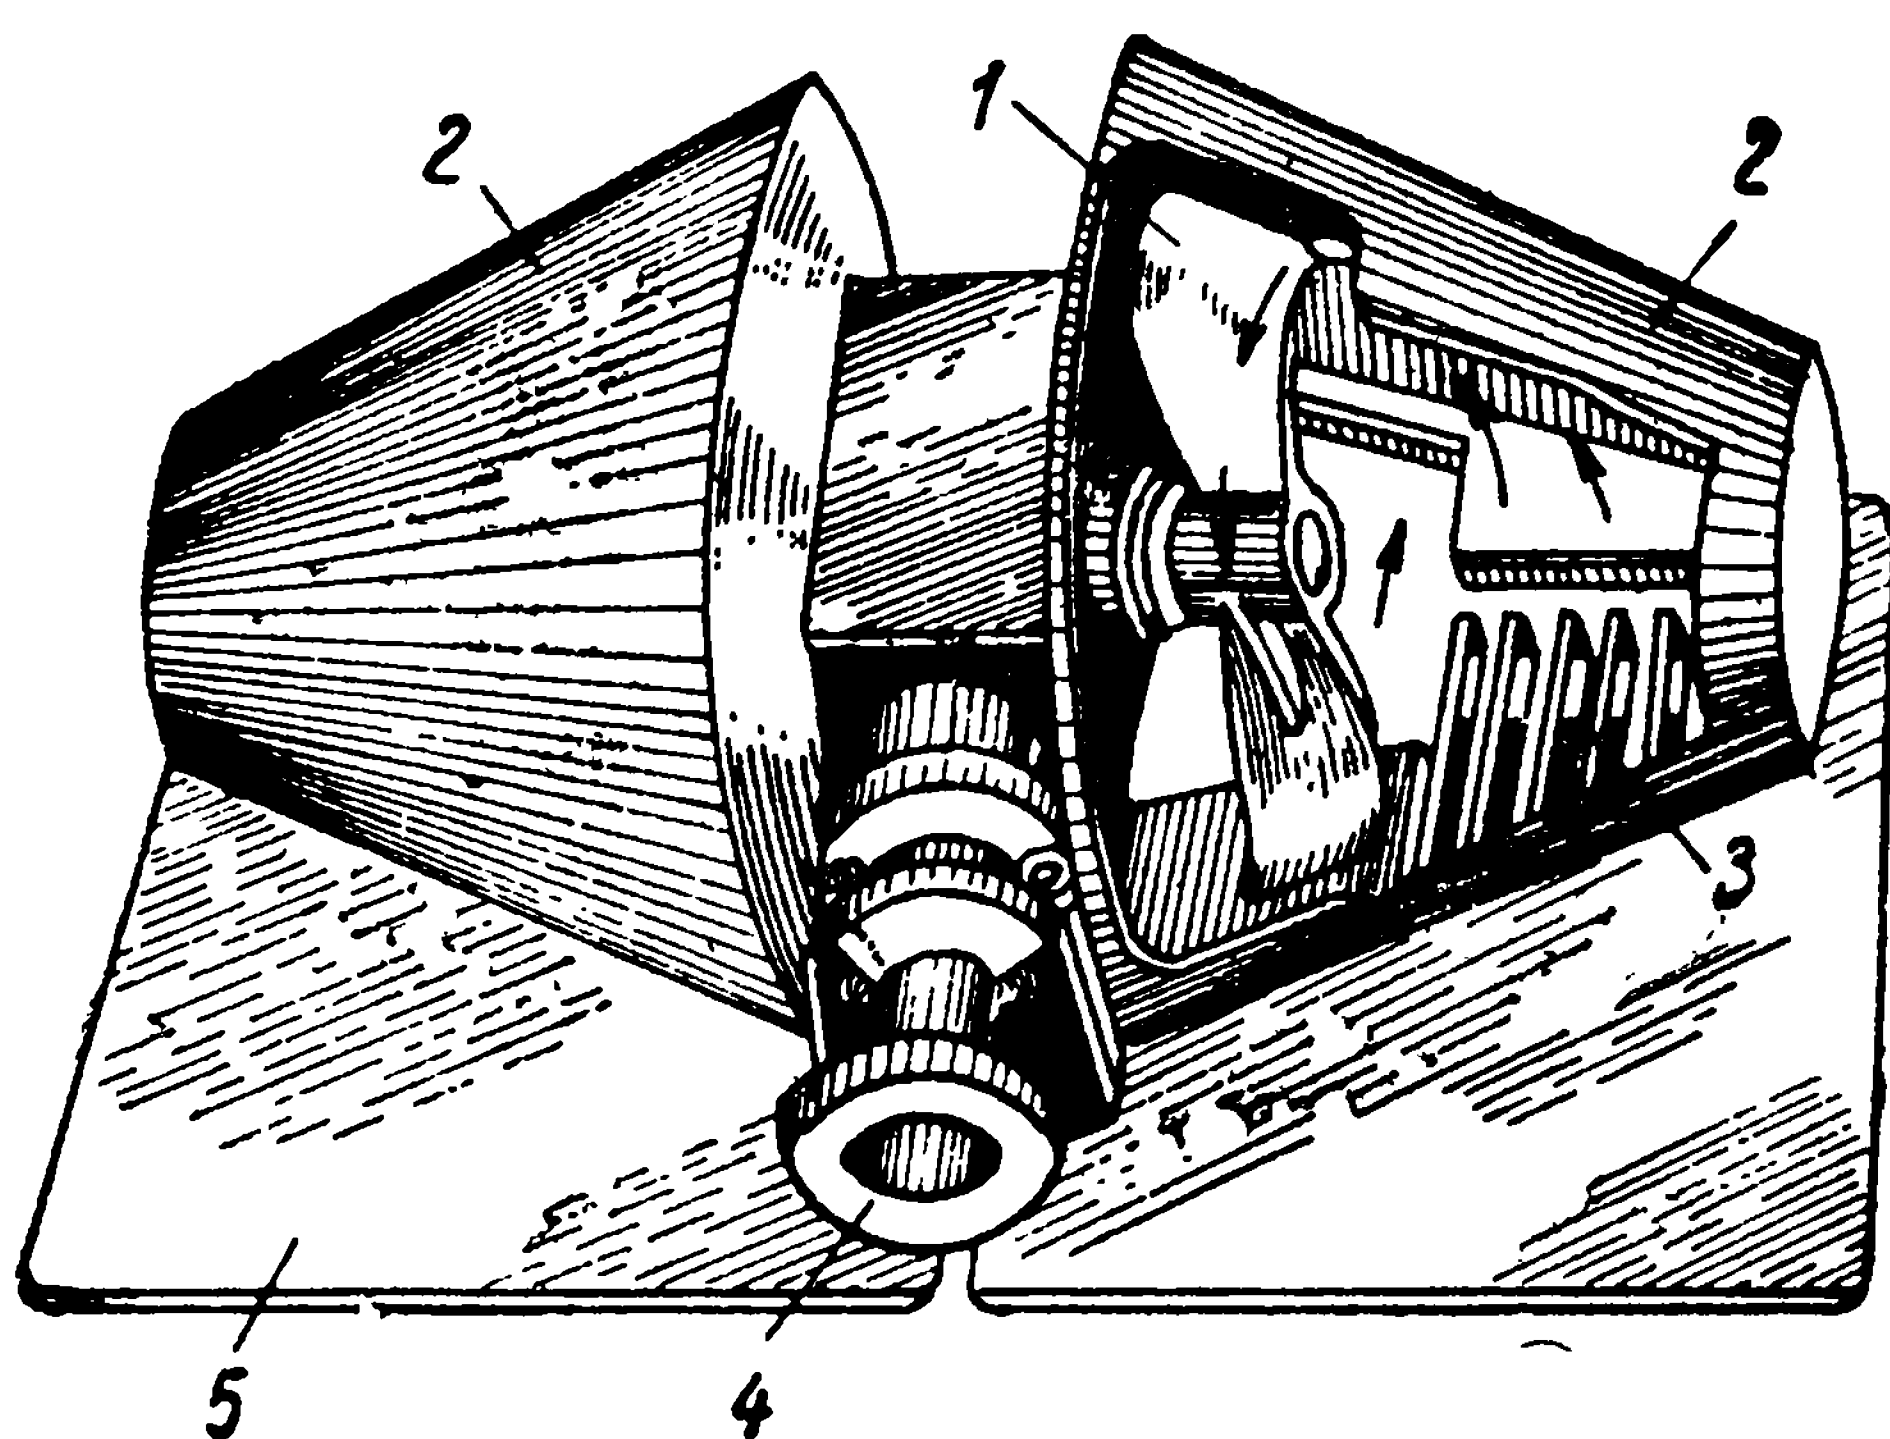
Конусный движитель конструкции Гочкиса (1926 г.)
